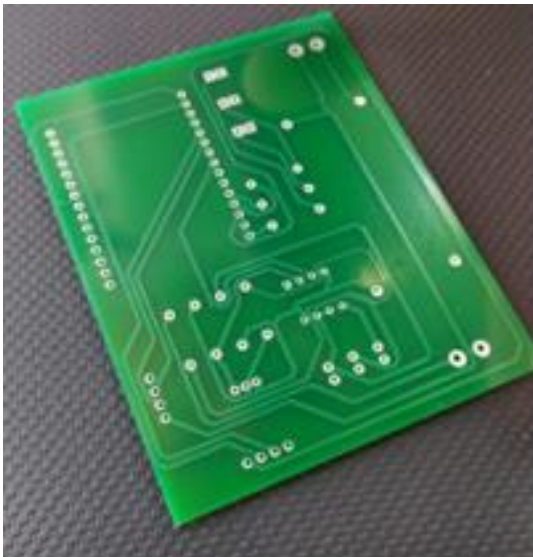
Representación 3D de la Placa de Circuito Impreso PCB.
